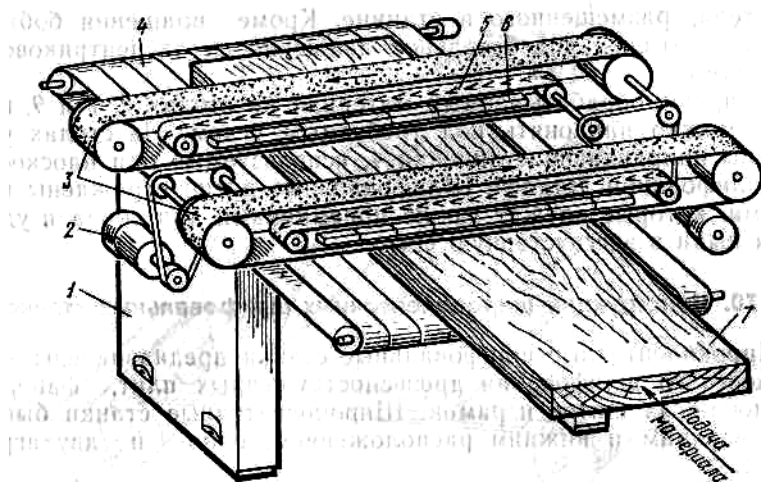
Схема двухленточного шлифовального станка с конвейерной подачей ШЛПС-9;
